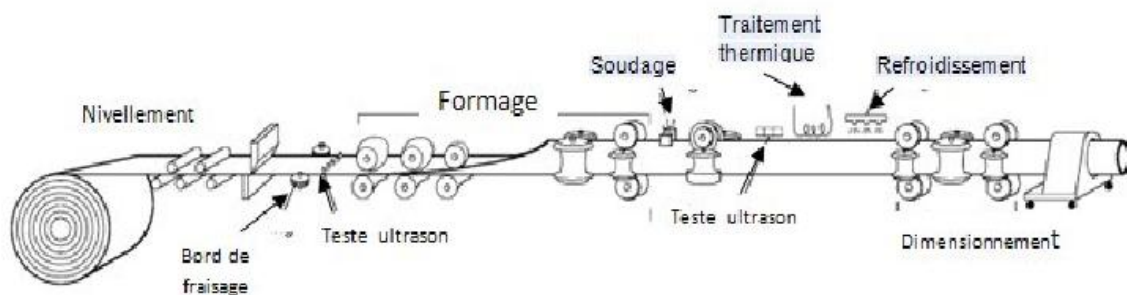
Technique de fabrication des tubes soudés en spirale.
